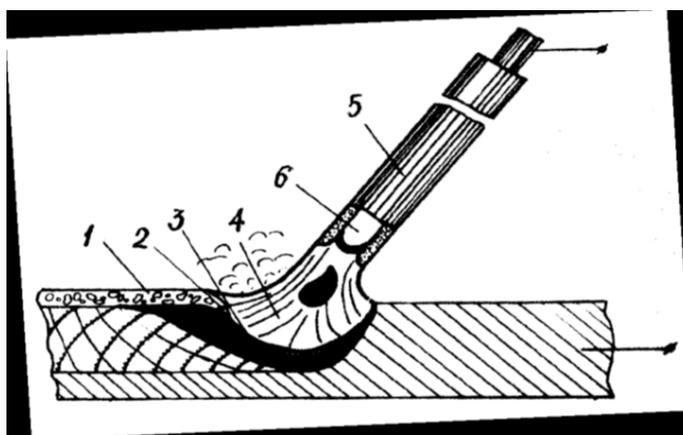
Схема ручной дуговой сварки: 1 – затвердевший шлак; 2 – сварочная ванна; 3 – слой расплавленного шлака; 4 – столб дуги; 5 – обмазка на электроде; 6 – металлический стержень (электрод)
